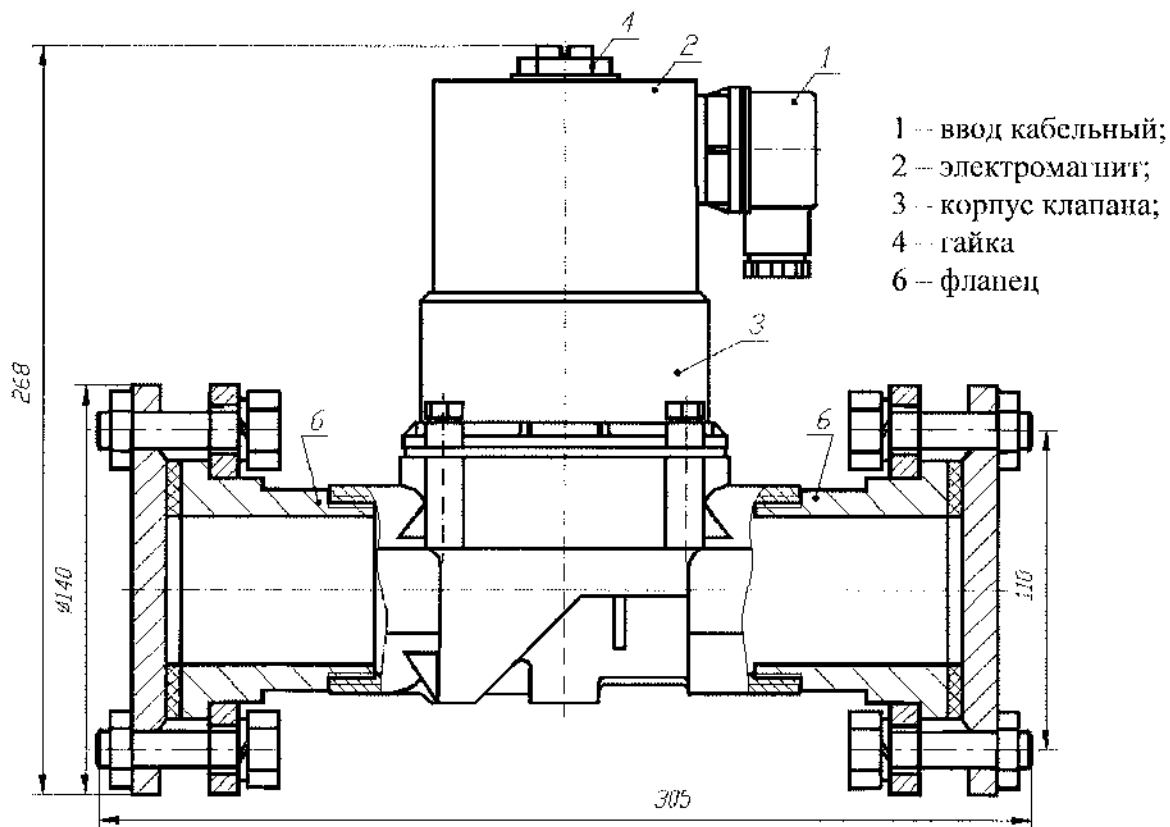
Габаритные и установочные размеры клапана КГЭЗ-50
